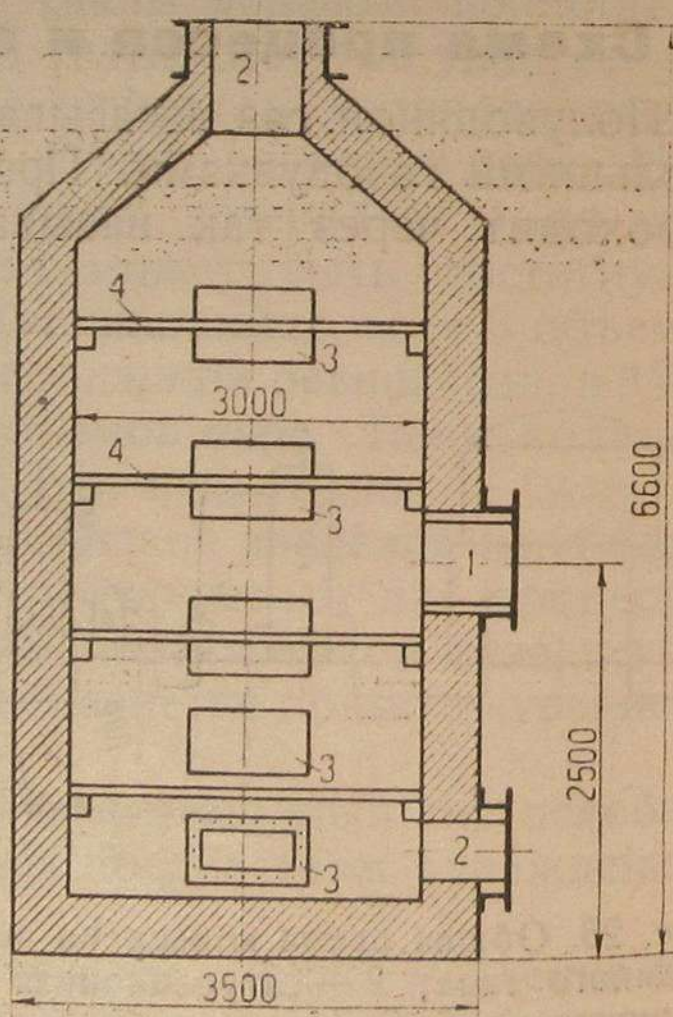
Конвертор окиси углерода (CO): 1 — вход газа; 2 — выход газа; 3 — люки; 4 — колонки для катализатора.
